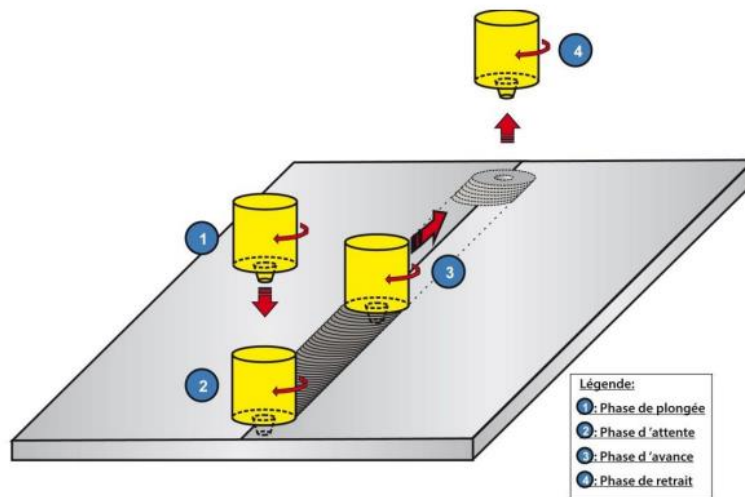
Les étapes du soudage FSW [1]
